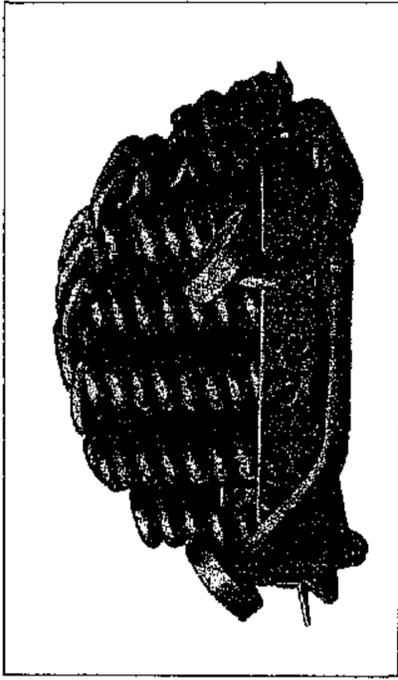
/4: Dampfüberhitzer-Paket für den Rauchkammereinbau
